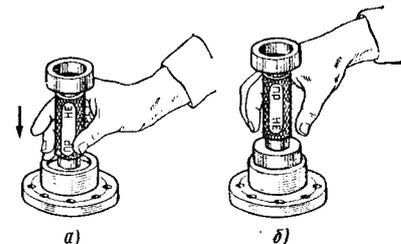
Прием проверки отверстий предельной пробкой-калибром:
